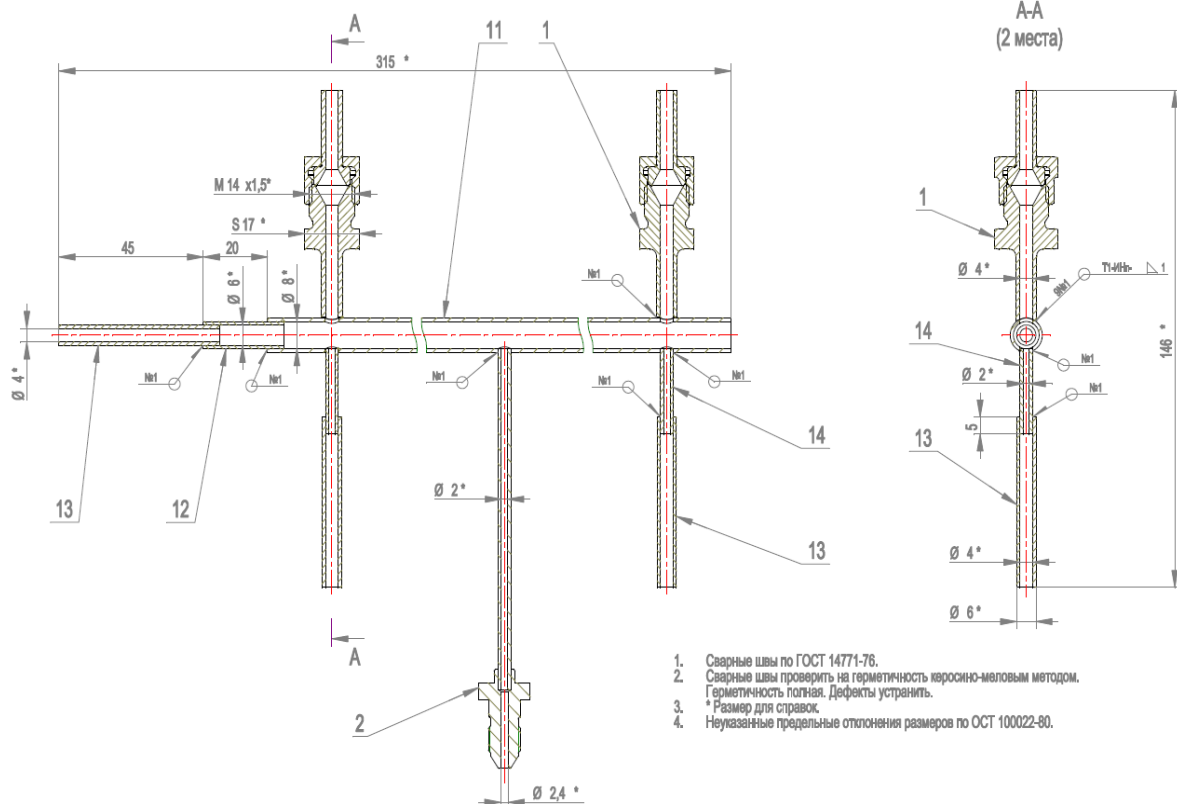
Фрагмент сборочного чертежа гладкой трубки
